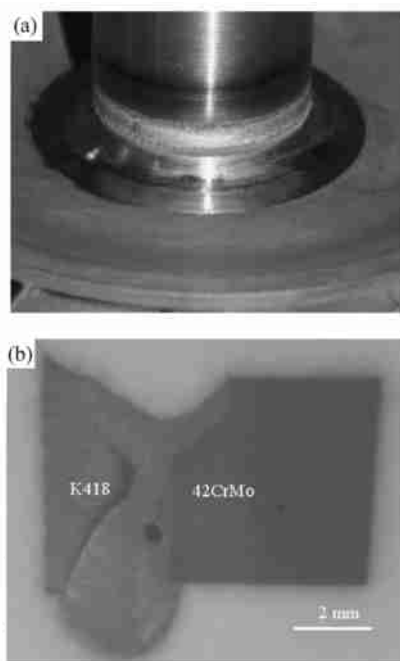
K418 涡轮盘和 42CrMo 转轴激光焊接焊缝宏观形貌 (a) 和横截面形貌 (b)
